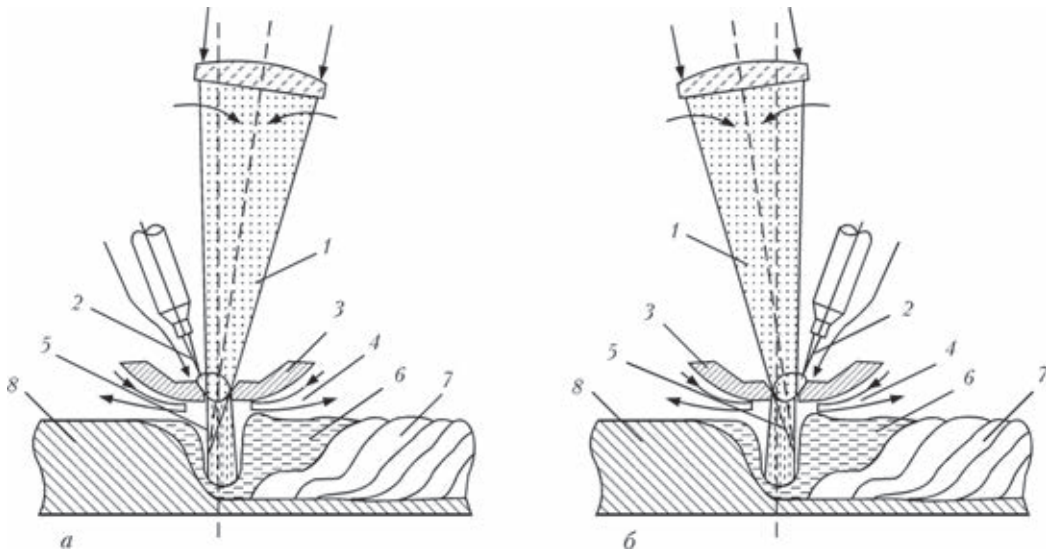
Схемы процесса гибридной лазерно-плазменной сварки с расположением плазменной горелки перед (а) и за (б) лазерным пучком [15]: 1 — сфокусированное лазерное излучение; 2 — неплавящийся электрод; 3 — плазмообразующее сопло; 4 — защитный газ; 5 — плазменный разряд; 6 — сварочная ванна; 7 — металл шва; 8 — основного металла
